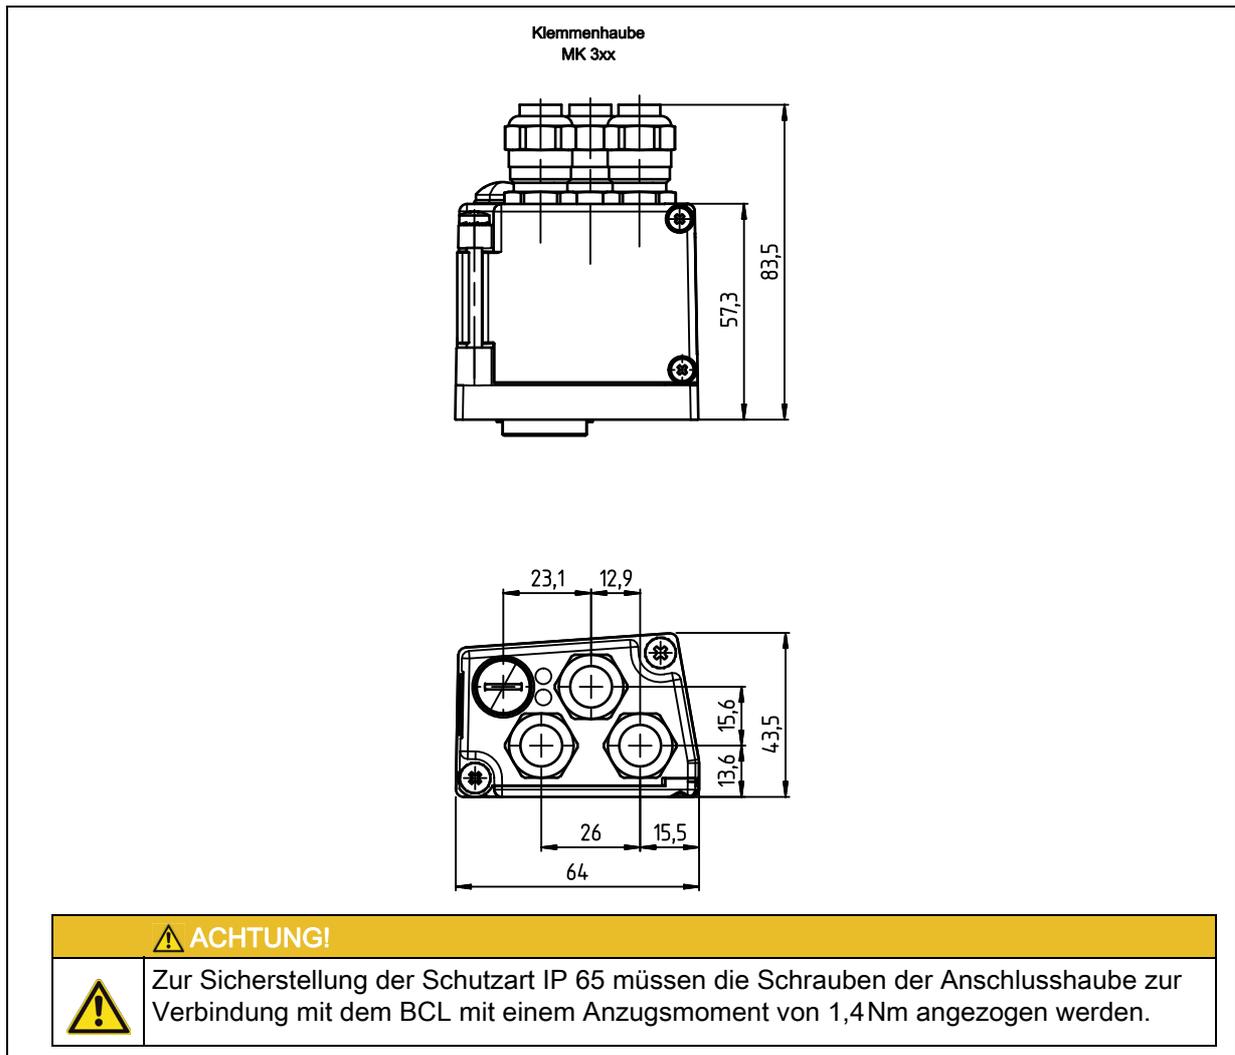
Maßzeichnung Klemmenhaube MK 3xx
